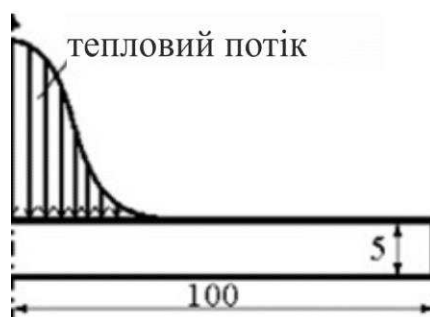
Загальний вигляд досліджуваного зразка
